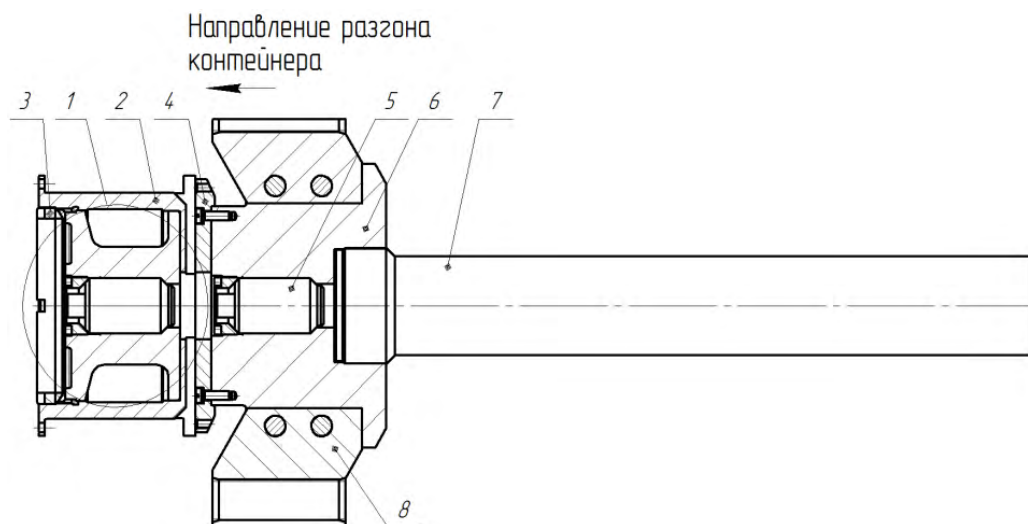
Схема контейнера: 1 – ОИ; 2 – корпус; 3 – кольцо; 4 – плита; 5 – датчик ускорений; 6 – основание; 7 – шток; 8 – башмак
